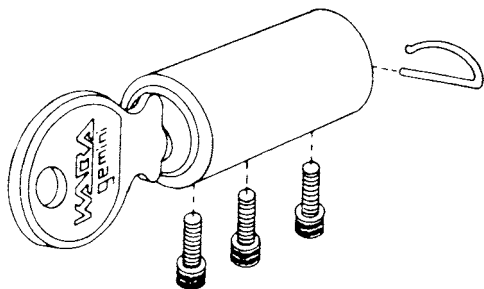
В корпусе цилиндра ручки-кнопки есть три винта для крепления вставки (С разрешения компании Lori Corporation)
